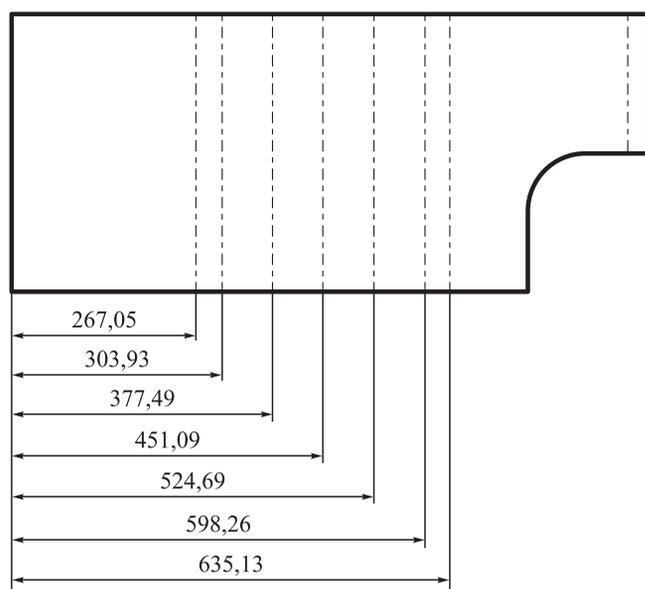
Развернутый вид деформируемой заготовки с указанием линий изгиба
